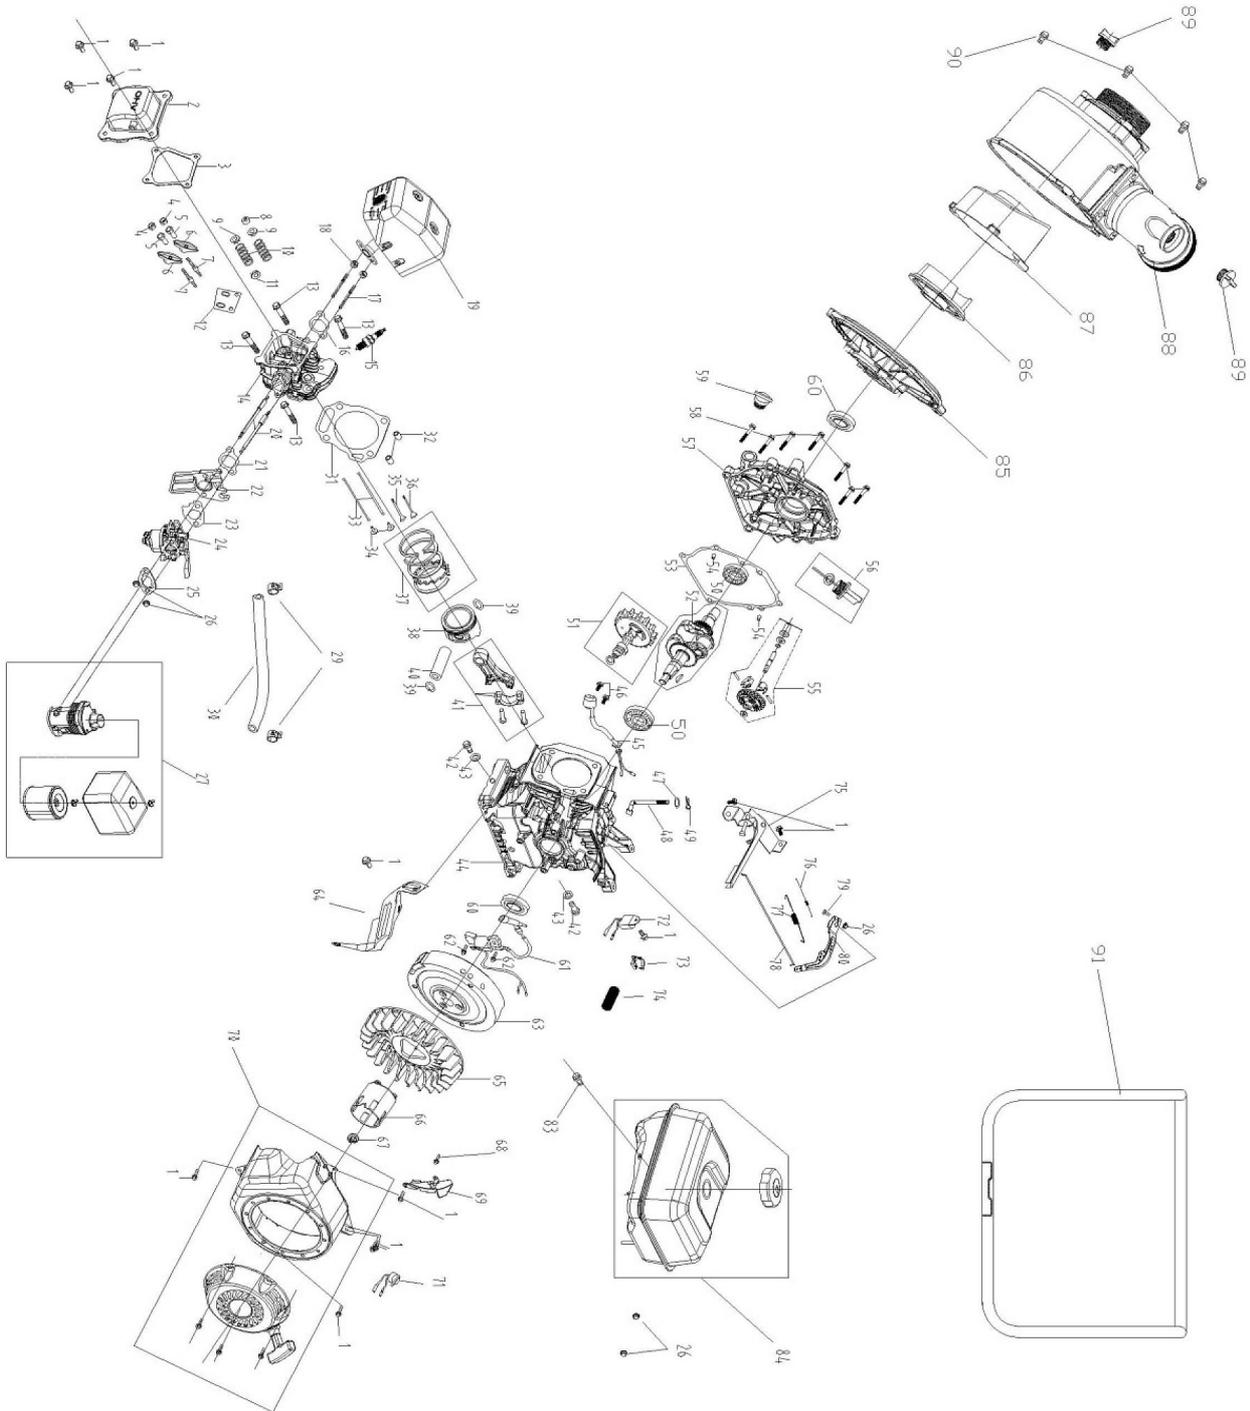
Piezas de dibujo FWP 50 y 80 partes
